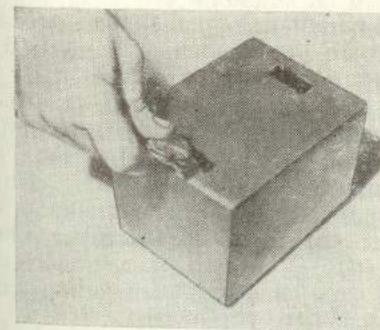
Приспособление РТПО-9 для завода пружин наручных часов
